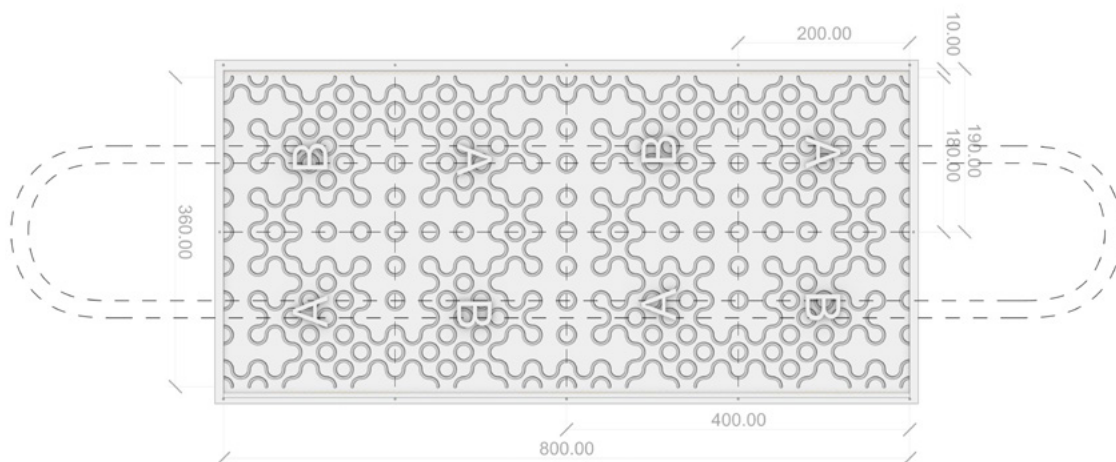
Diseño de moldes mediante proceso de diseño paramétrico.
